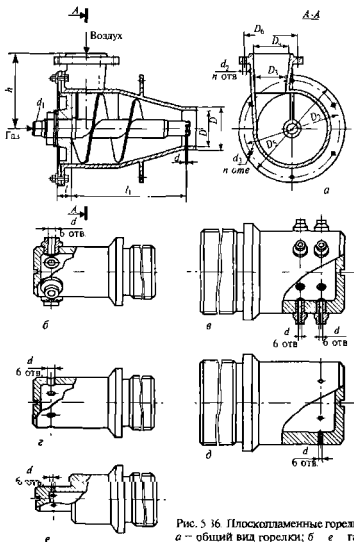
36. Плоскопламенные горелки типа ГПП: а — общий вид горелки; б — е — газовые сопла
